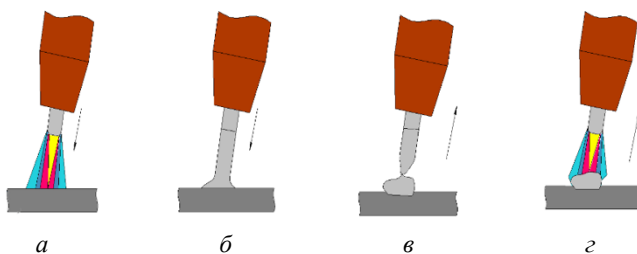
Основной принцип СМТ-процесса: *а* – дуга горит между проволокой и изделием; *б–в* – отрыв капли за счет обратного перемещения сварочной проволоки; *г* – возобновление горения дуги
